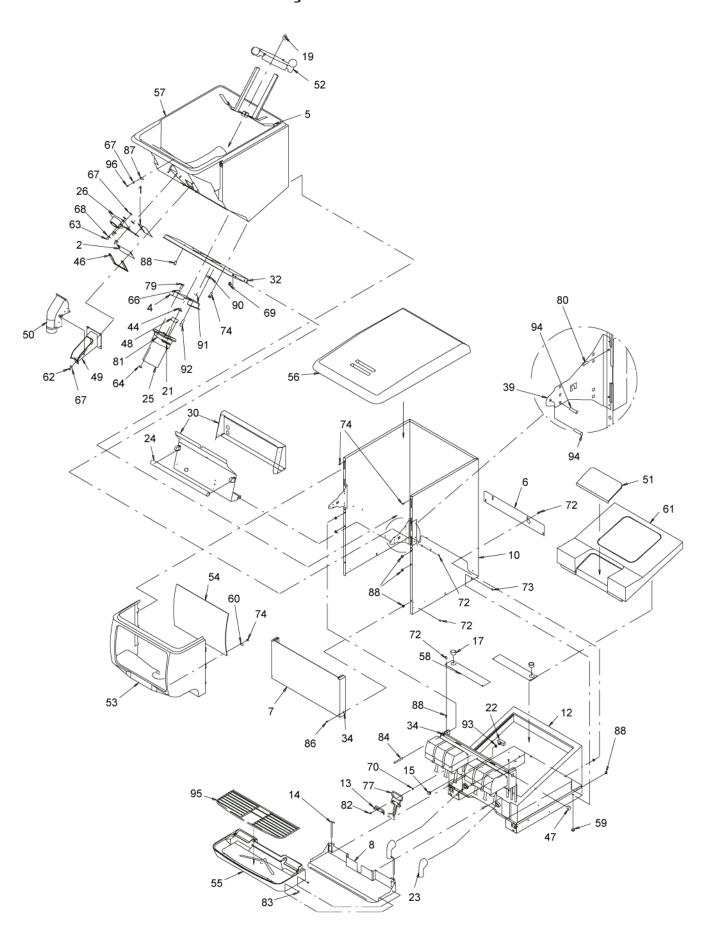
SEÇÃO DO GABINETE - VISÃO EXPLODIDA
